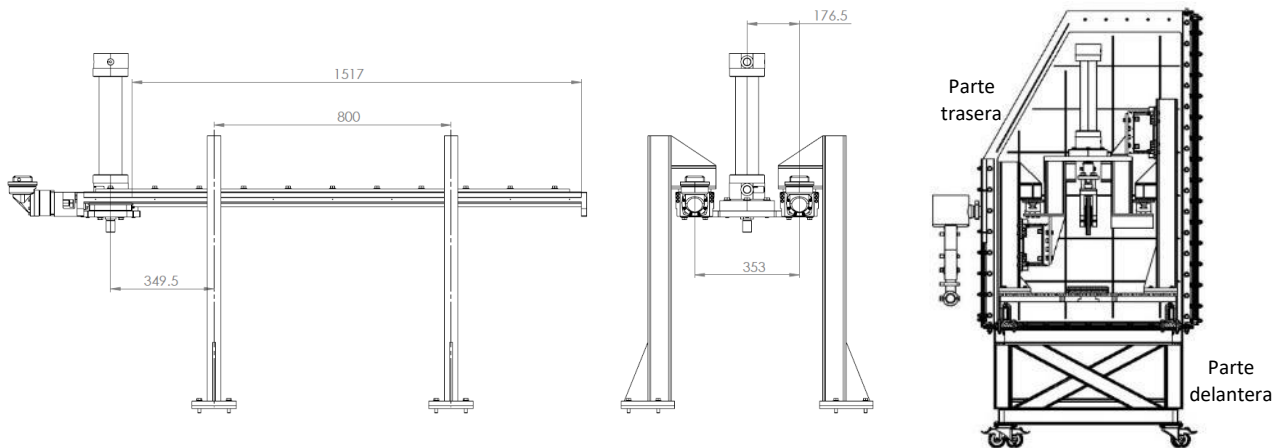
Diferentes diseños de micro-laminador. Izquierda: diseño inicial. Derecha: diseño asimétrico con sistema de guiado en la parte interna de los pilares
